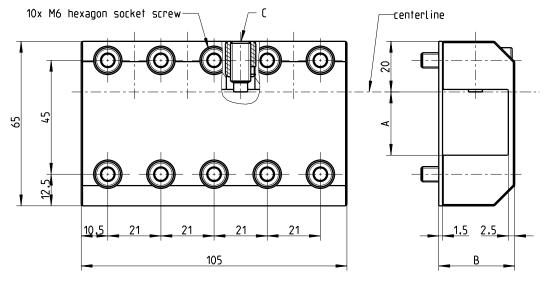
Werkzeughalter für Drehmeissel für axial montiertes Dynamometer, Typ 9129AE...
